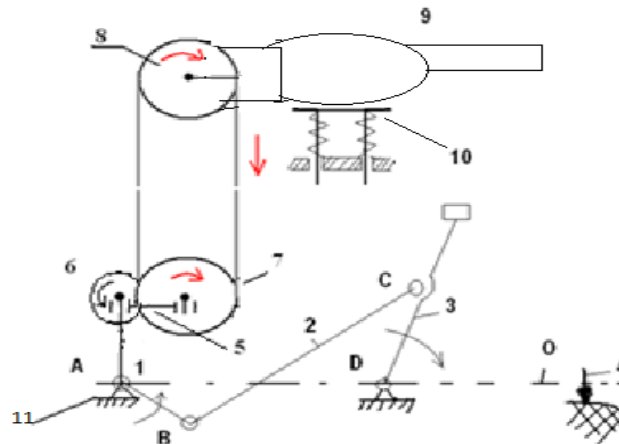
Схема ударной машины с приводом от УШМ: 1–4 – детали РУМ С. Абдраимова, 5 – серьга, 6 – шестерня кривошипа, 7 – ведомая шкив-шестерня, 8 – ведущий шкив УШМ, 9 – УШМ, 10 – виброплита, 11 – корпус молотка
